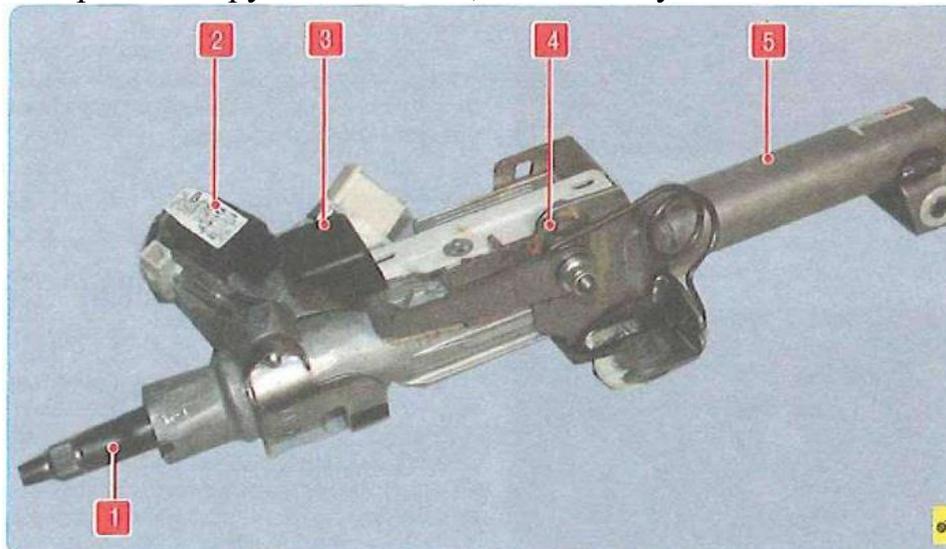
Рулевая колонка: 1 - вал рулевой колонки; 2 - выключатель (замок) зажигания; 3 - рычаг регулировки положения рулевой колонки; 4 - механизм регулировки положения рулевой колонки; 5 - корпус рулевой колонки
